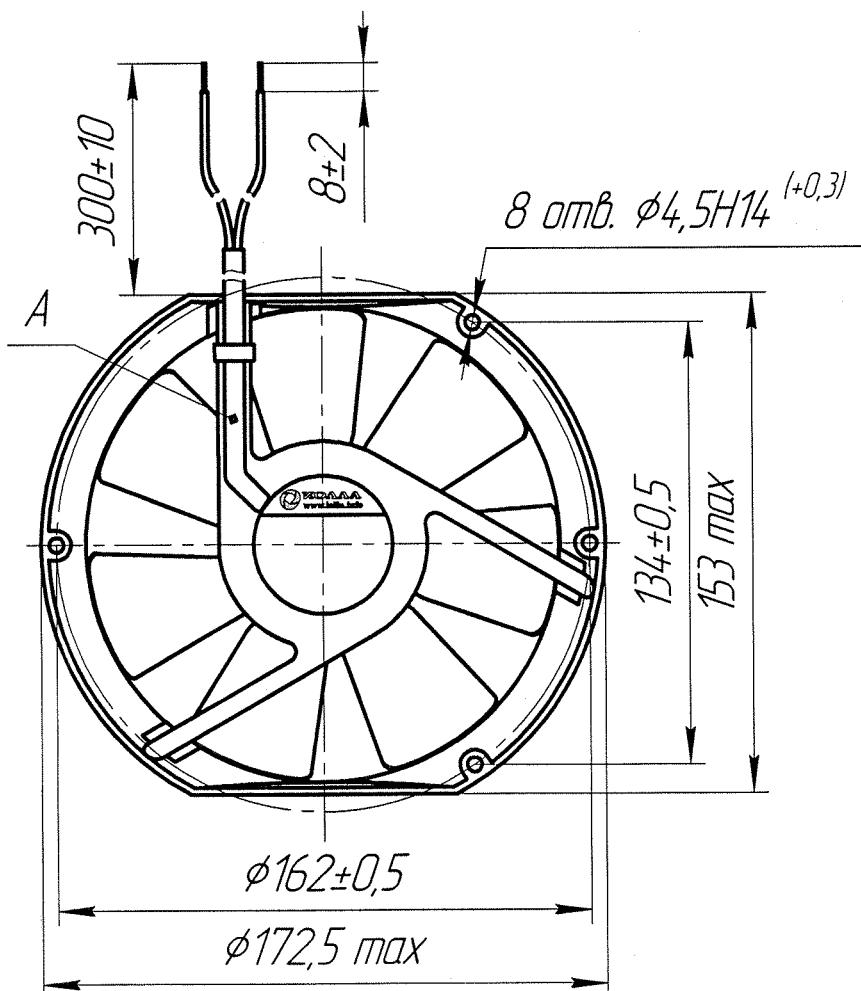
Габаритные, установочные и присоединительные размеры вентилятора 11ЭВ-14-3-4215, 11ЭВ-14-3-4225 и 11ЭВ-2-10-4425.
